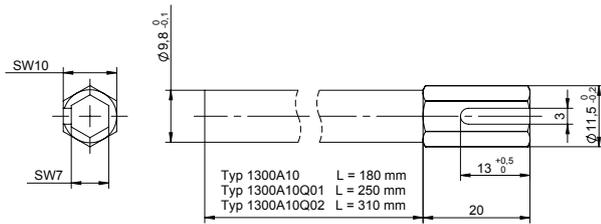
Montageschlüssel SW10/SW7 Typ 1300A10...
